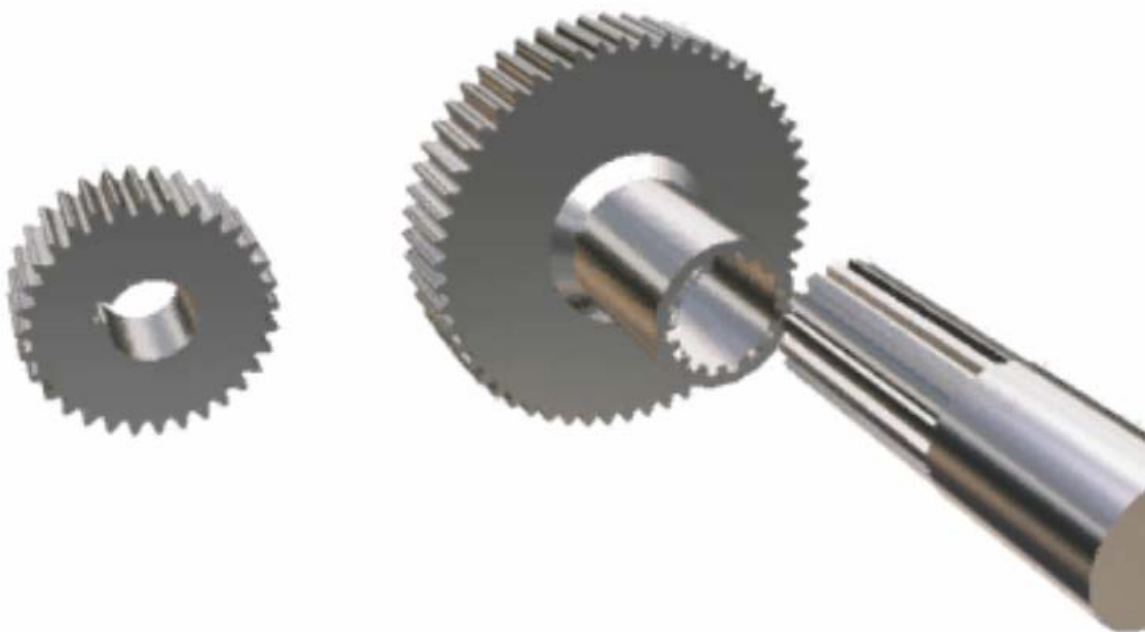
Детали зубчатой передачи со шлицевым соединением
